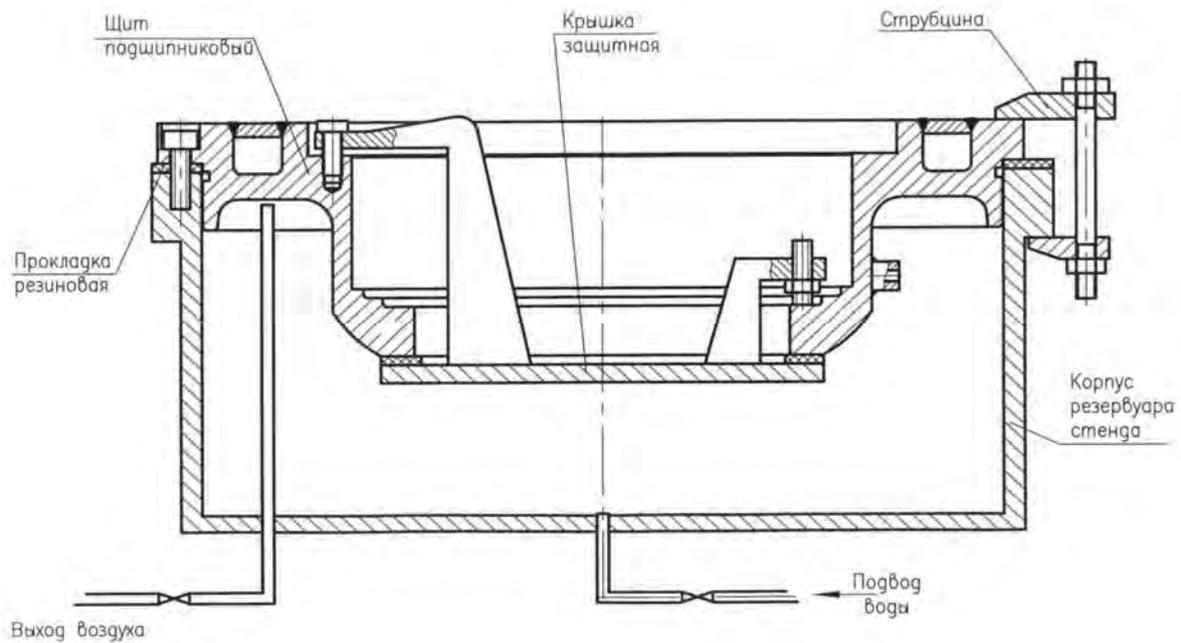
Схема гидравлических испытаний подшипникового щита электродвигателя
